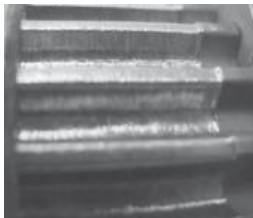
Пример обработки цилиндрической поверхности при износе зубьев реечного колеса и рейки токарного станка
